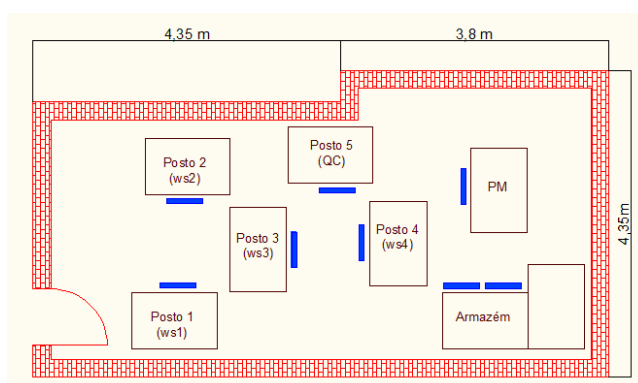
Layout utilizado na iteração da ferramenta Organização de Layout.
